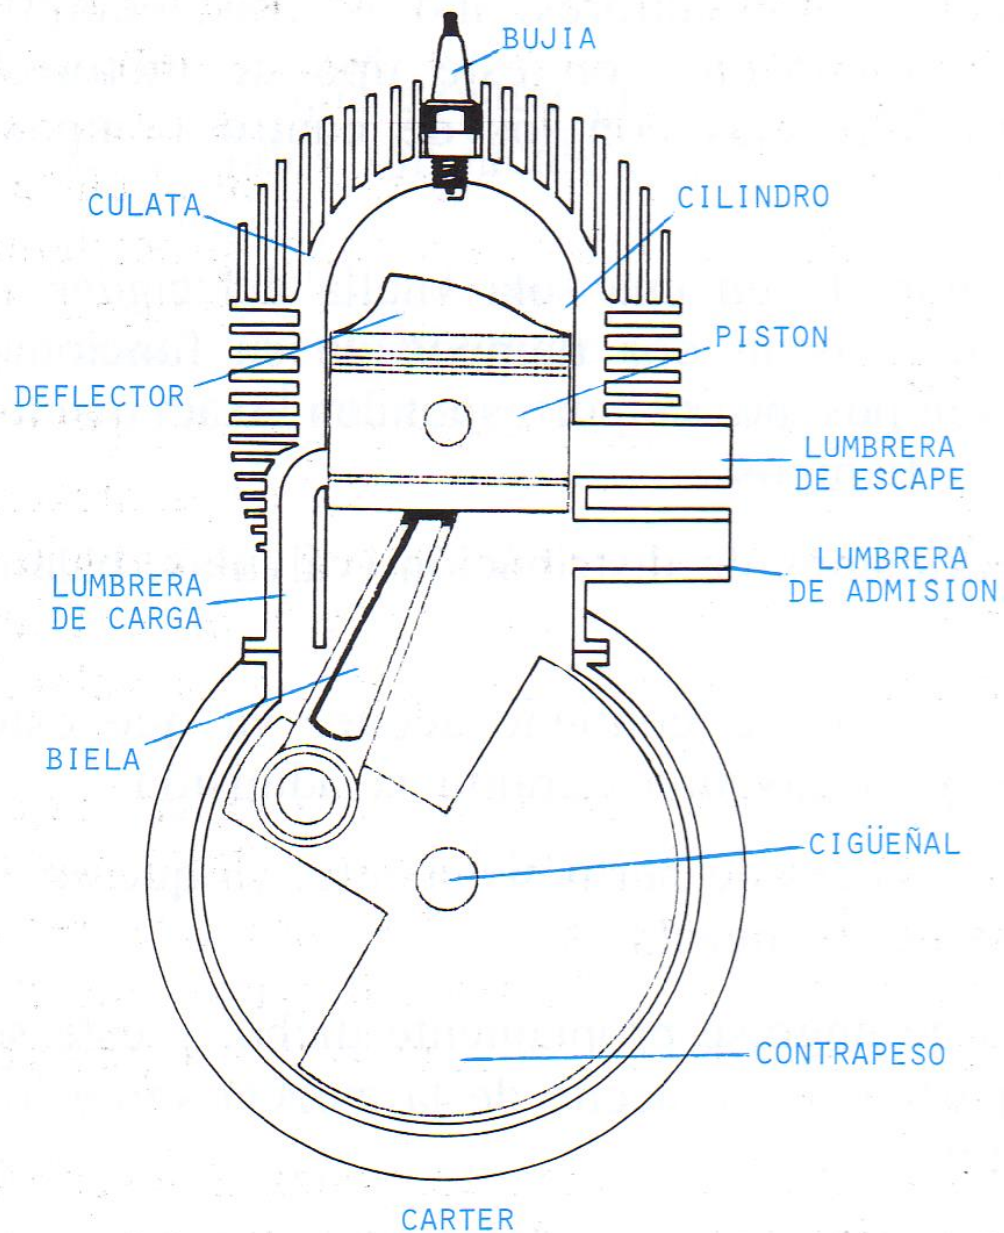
Partes de que consta el motor de dos tiempos.
